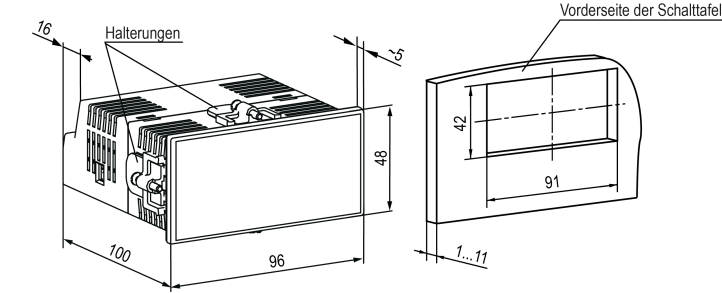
Abmessungen des P2-Gehäuses und des Montageausschnitts
